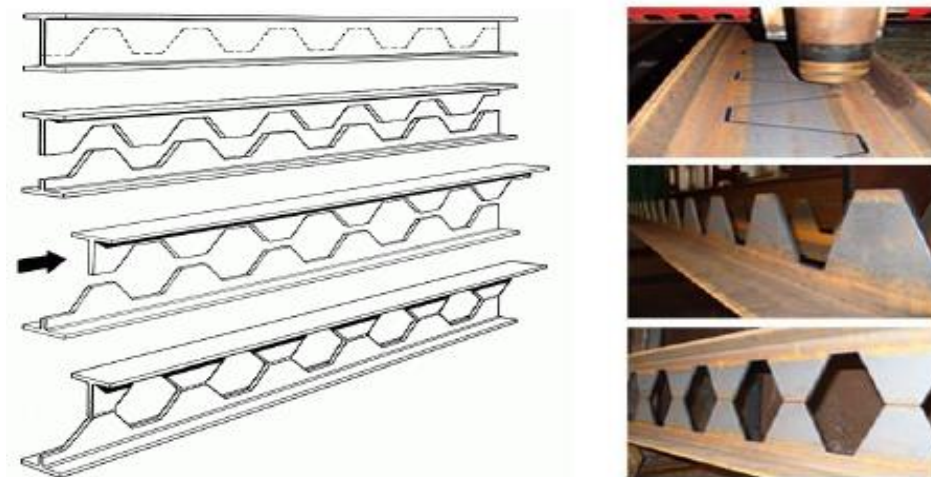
Processo de corte e soldadura de vigas alveoladas (Grünbauer, 2010)
